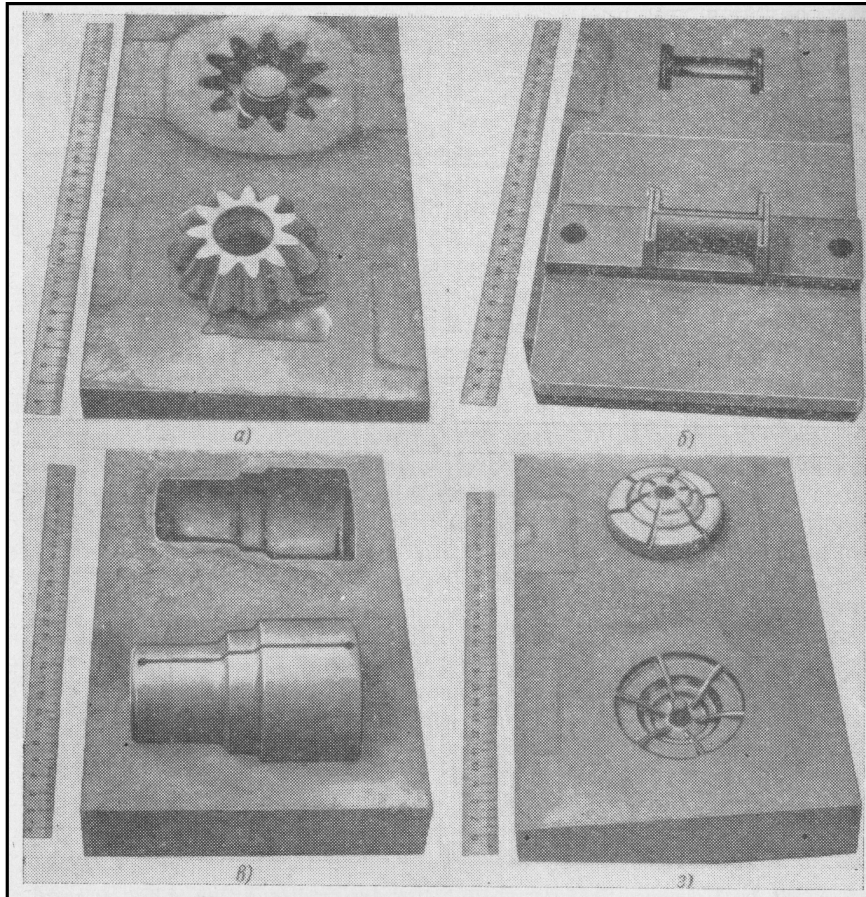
Порожнини кувальних штампів після ЕХО: а - для конічної шестерні; б - для пальця ланцюга; в - для ступінчастого валика; г - для розрізної кришки
